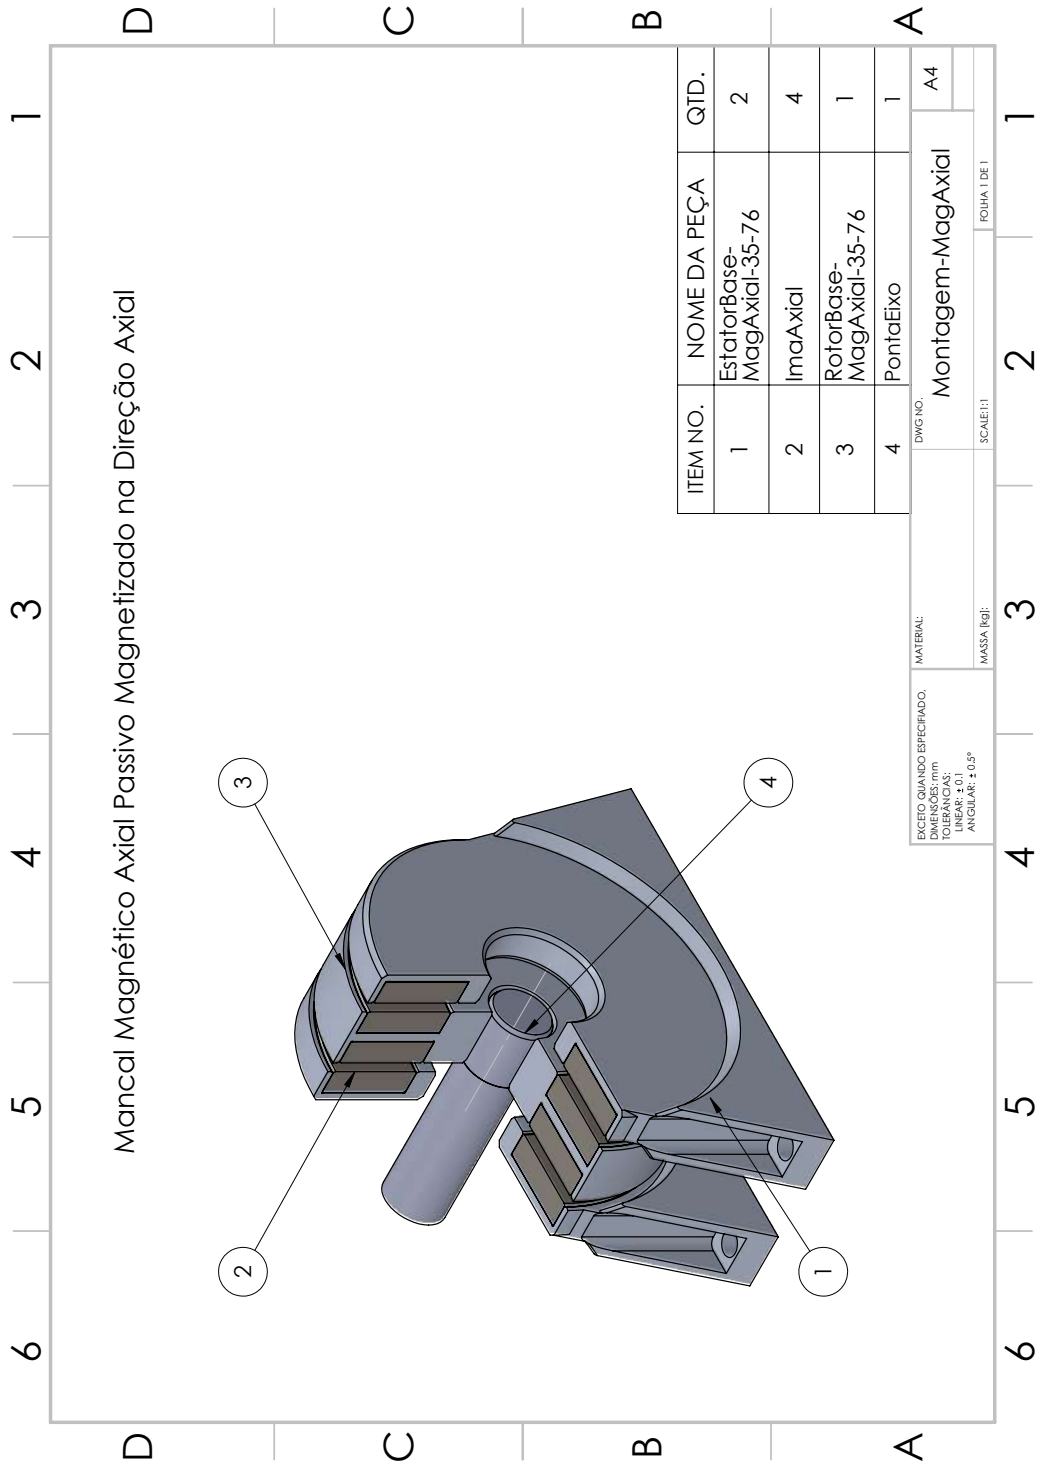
Ilustração do Desenho Mecânico: Mancal magnetizado na direção Axial – Rotor
